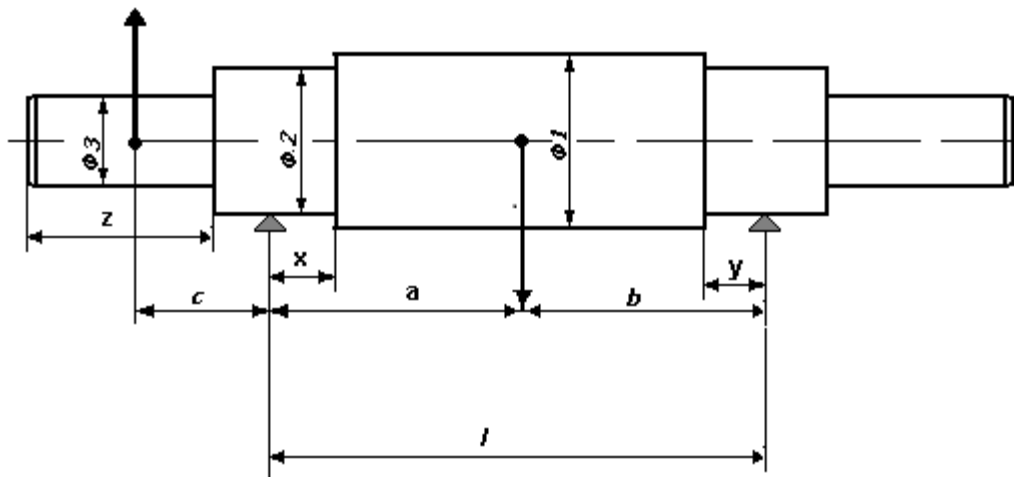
Конструкция и основные размеры вала для механического расчёта
